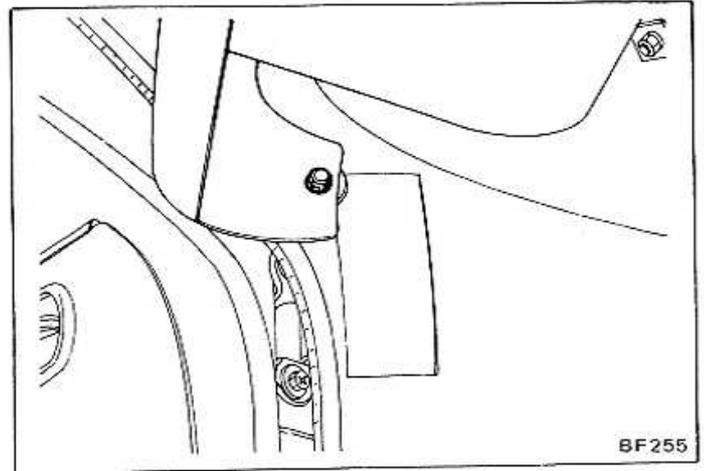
Vis de fixation de la planche de bord (Droit et gauche)
